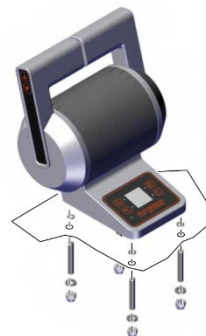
Desen explodat manetă de comandă la distanță a accelerației
